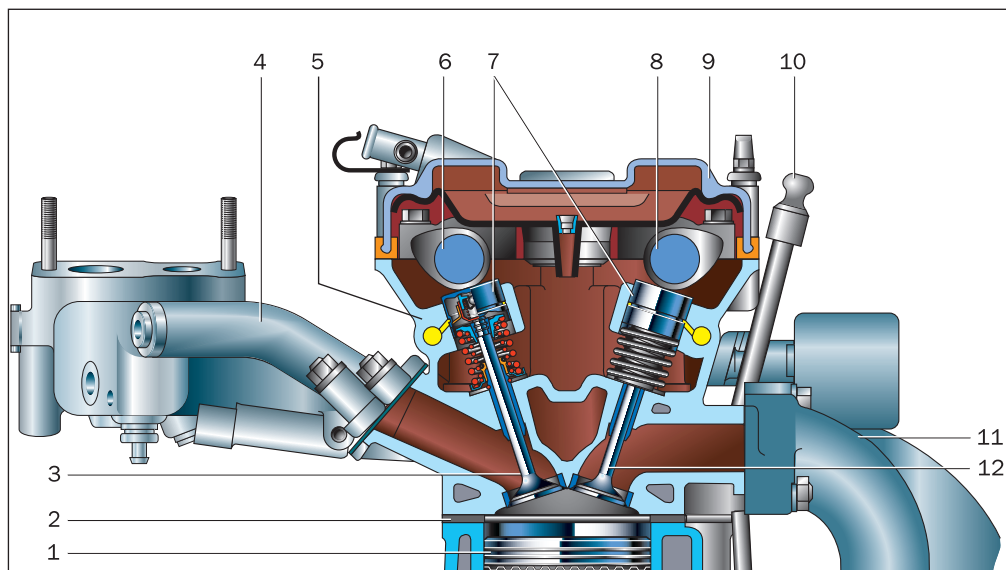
б. ГРМ двигателя 3М3-4063: 1 — поршень; 2 — прокладка головки блока цилиндров; 3 — впускной клапан; 4 — впускной трубопровод; 5 — головка блока цилиндров; 6 — распределительный вал впускных клапанов; 7 — гидротолкатели; 8 — распределительный вал выпускных клапанов; 9 — крышка головки блока цилиндров; 10 — масломерный щуп; 11 — выпускной коллектор; 12 — выпускной клапан
